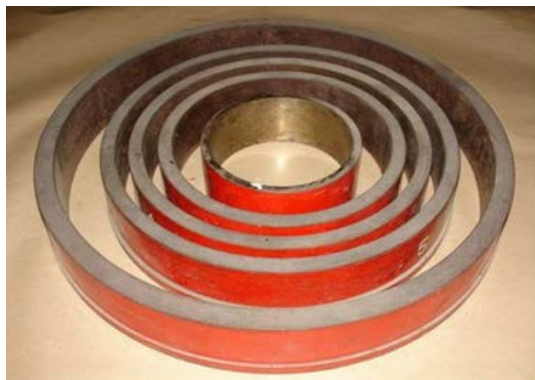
Общий вид пяти эталонных колец для градуировки и калибровки каверномеров-профилемеров
